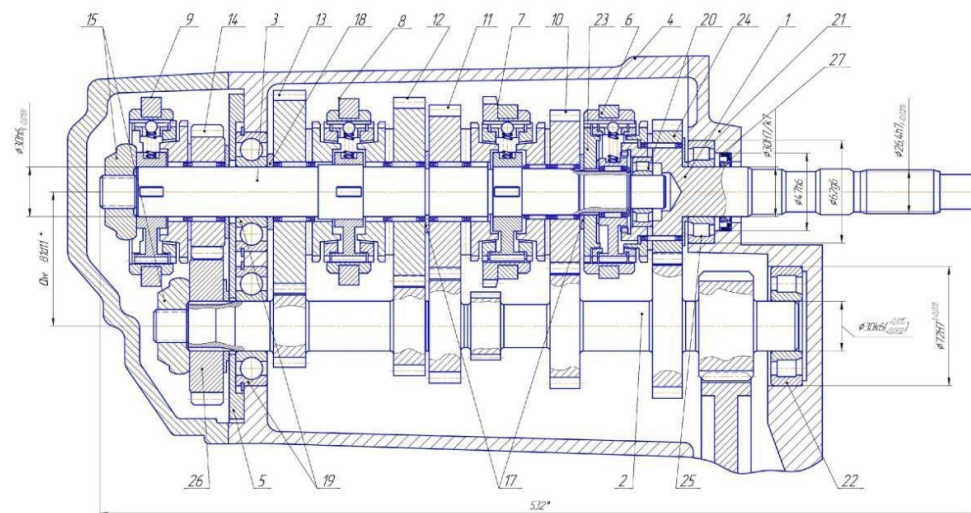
Складальний кресленник розробленої трьохвальної коробки передач:
